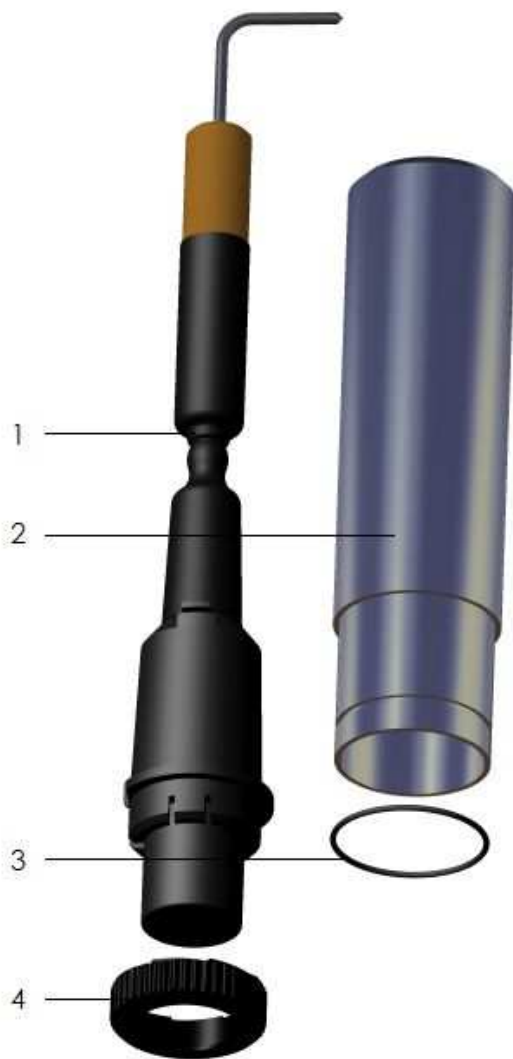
Vue éclatée de l'assemblage du brûleur FB7
